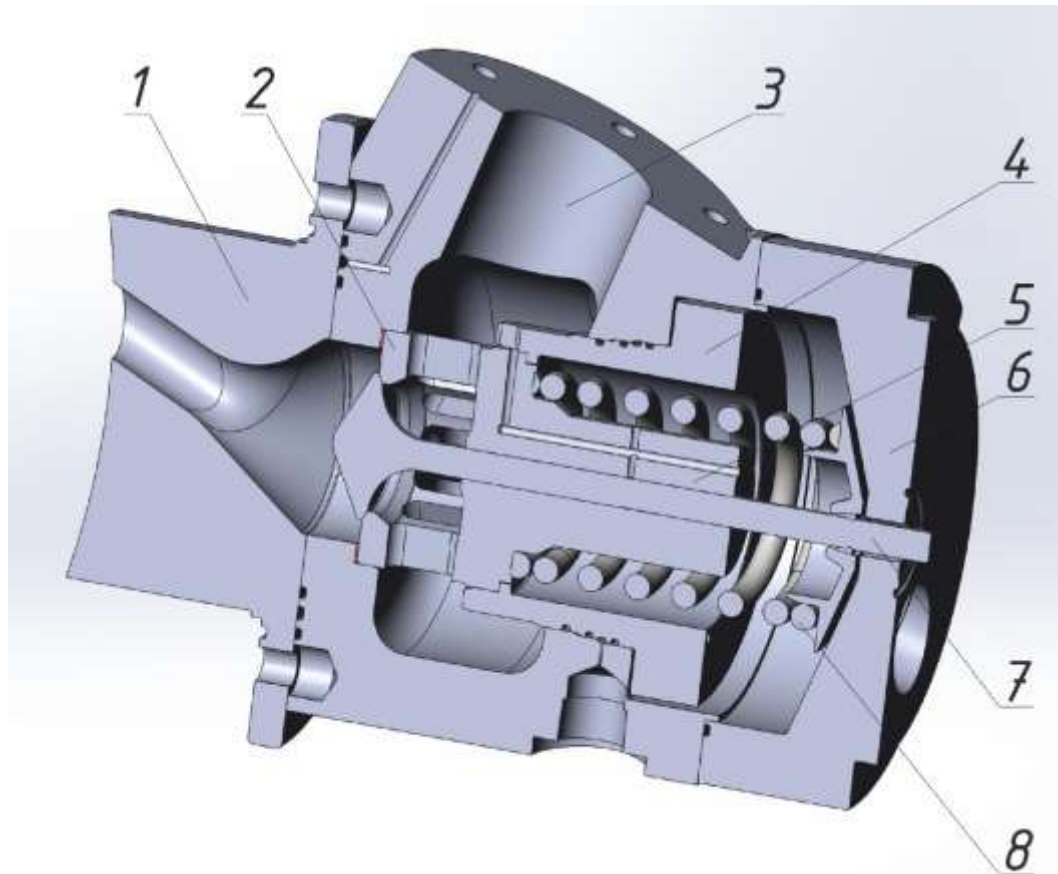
Трехмерная модель газового клапана двигателя W-X62DF фирмы WinGD, выполненная в среде SolidWorks: 1 – сопловая вставка; 2 – седло газового клапана; 3 – канал подвода газового топлива; 4 – корпус газового клапана; 5 – направляющая газового клапана; 6 – крышка; 7 – газовый клапан; 8 – возвратная пружина
